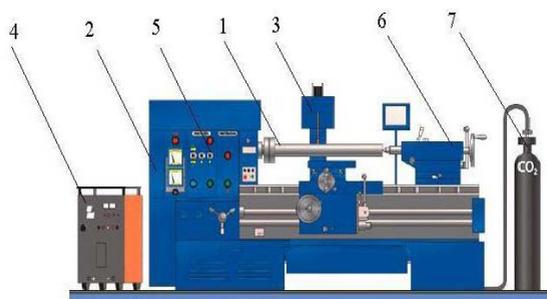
Схема типовой установки для автоматической наплавки цилиндрических деталей порошковой проволокой: 1 – наплавляемая деталь; 2 – манипулятор-вращатель; 3 – сварочная головка; 4 – источник питания; 5 – пульт управления; 6 – задняя бабка; 7 – баллон с защитным газом
